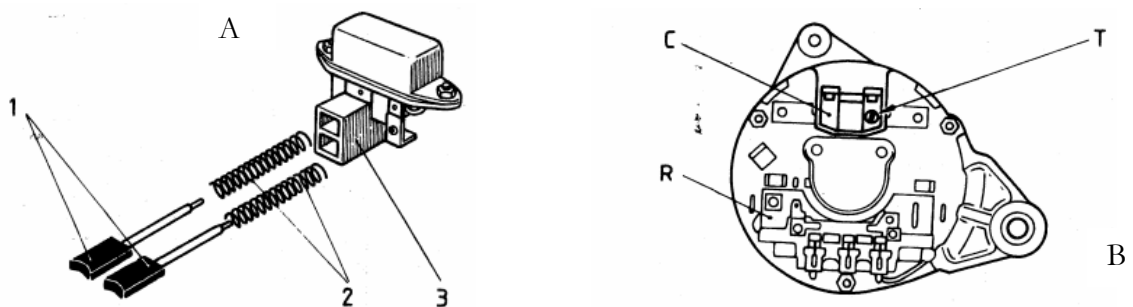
Conjunto de regulador incorporado com as escovas num alternador marca *Bosch* e sua posição no alternador ([6]).
